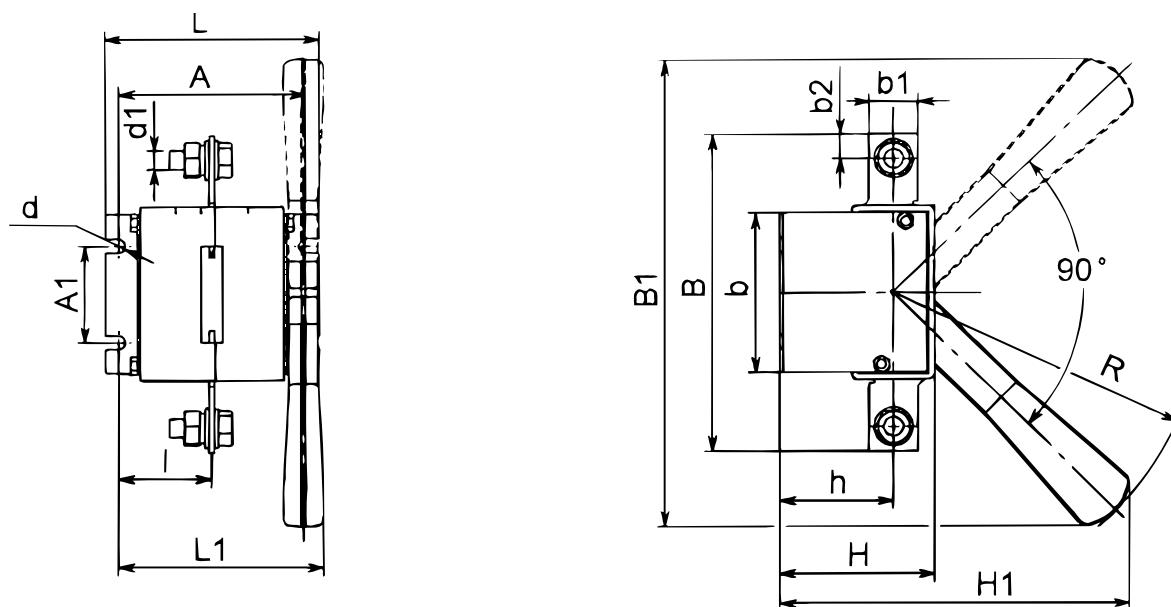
Выключатель-разъединитель однополюсный на одно направление с боковой рукояткой
